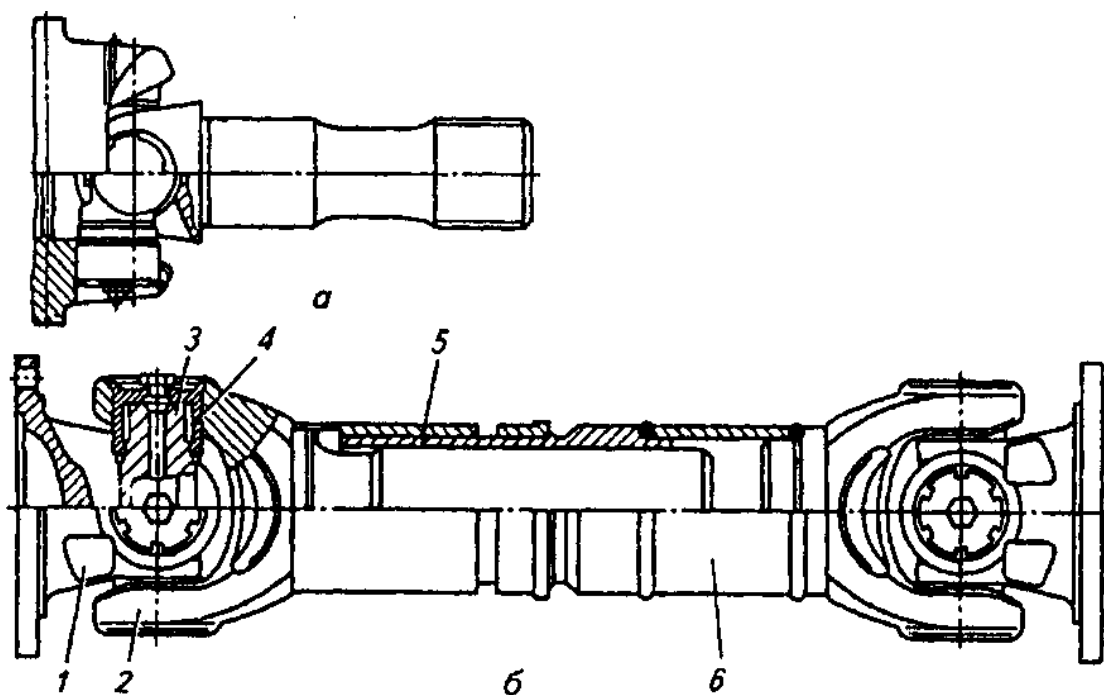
Карданные шарниры: а — простой; б — универсальный; 1 — ведущая вилка; 2 — ведомая вилка; 3 — крестовина; 4 — игольчатый подшипник; 5 — подвижное шлицевое соединение; 6 — труба карданного вала
